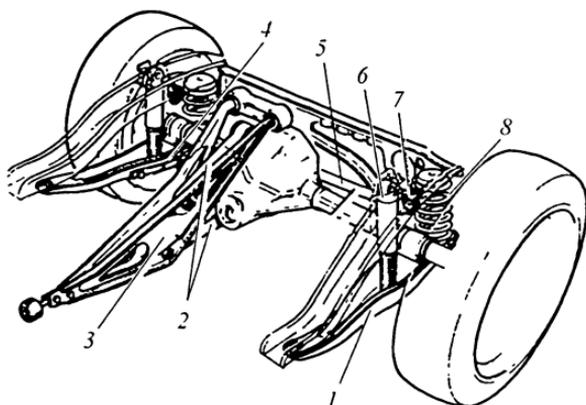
Детали задней подвески: 1 — продольный рычаг; 2 — реактивные тяги; 3 — подрамник; 4 — стабилизатор поперечной устойчивости; 5 — поперечина; 6 — амортизатор; 7 — жесткий упор штанги; 8 — пружина
